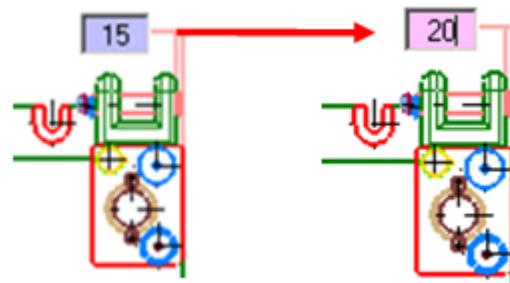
Döküm ölçülerı bölümü kısımları
